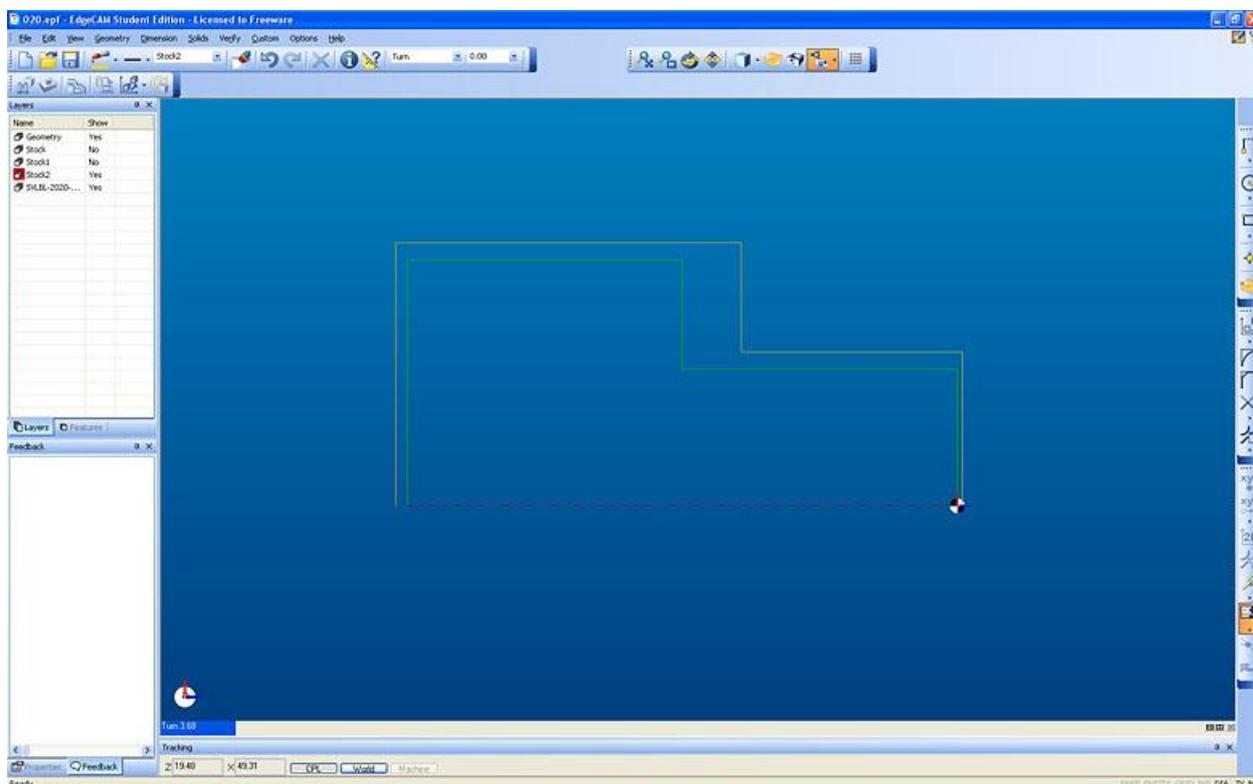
Edgcam. Создание заготовки для токарной обработки
